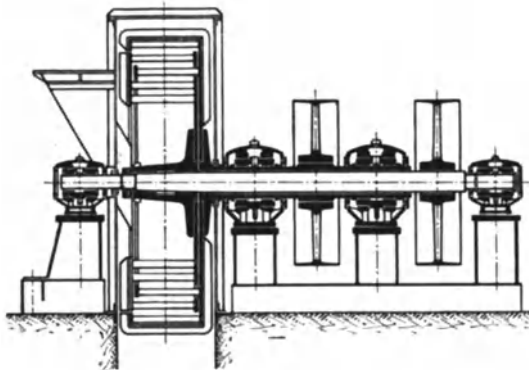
Desintegrator mit einseitigem Antrieb (Humboldt).
